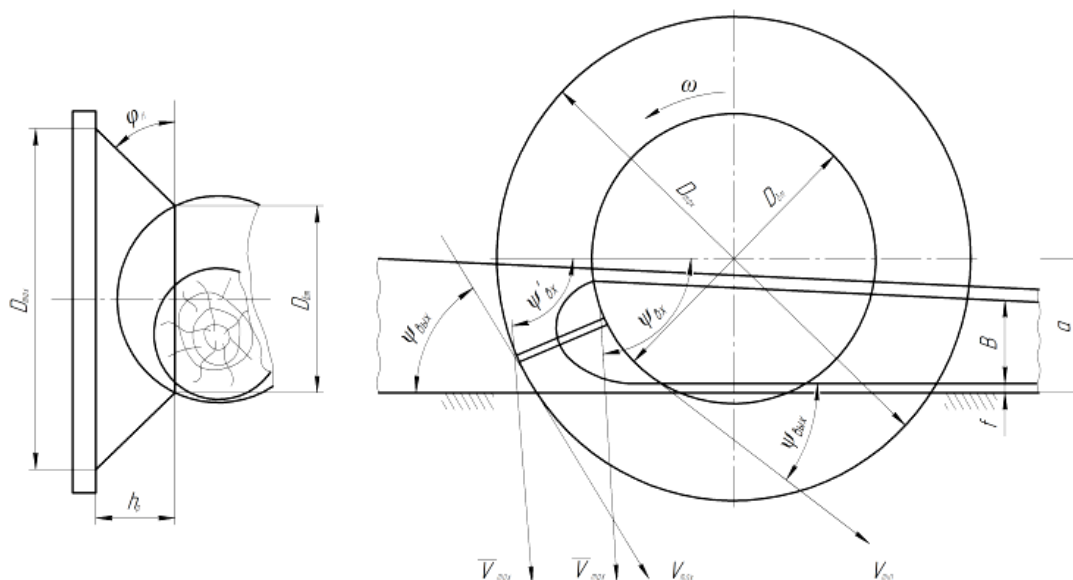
Параметры фрезерования древесины торцово-коническими фрезами
